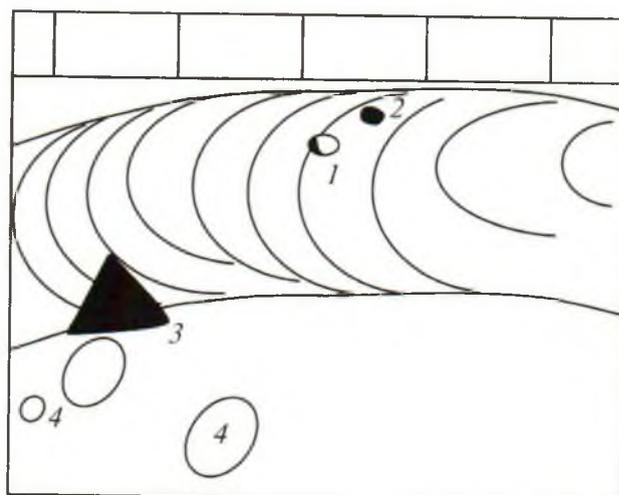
Пора 1 (газовая полость округлой формы) в стыковом сварном соединении трубопровода. Наблюдаются также шлаковое включение 2, неудаленный шлак 3, брызги металла 4
